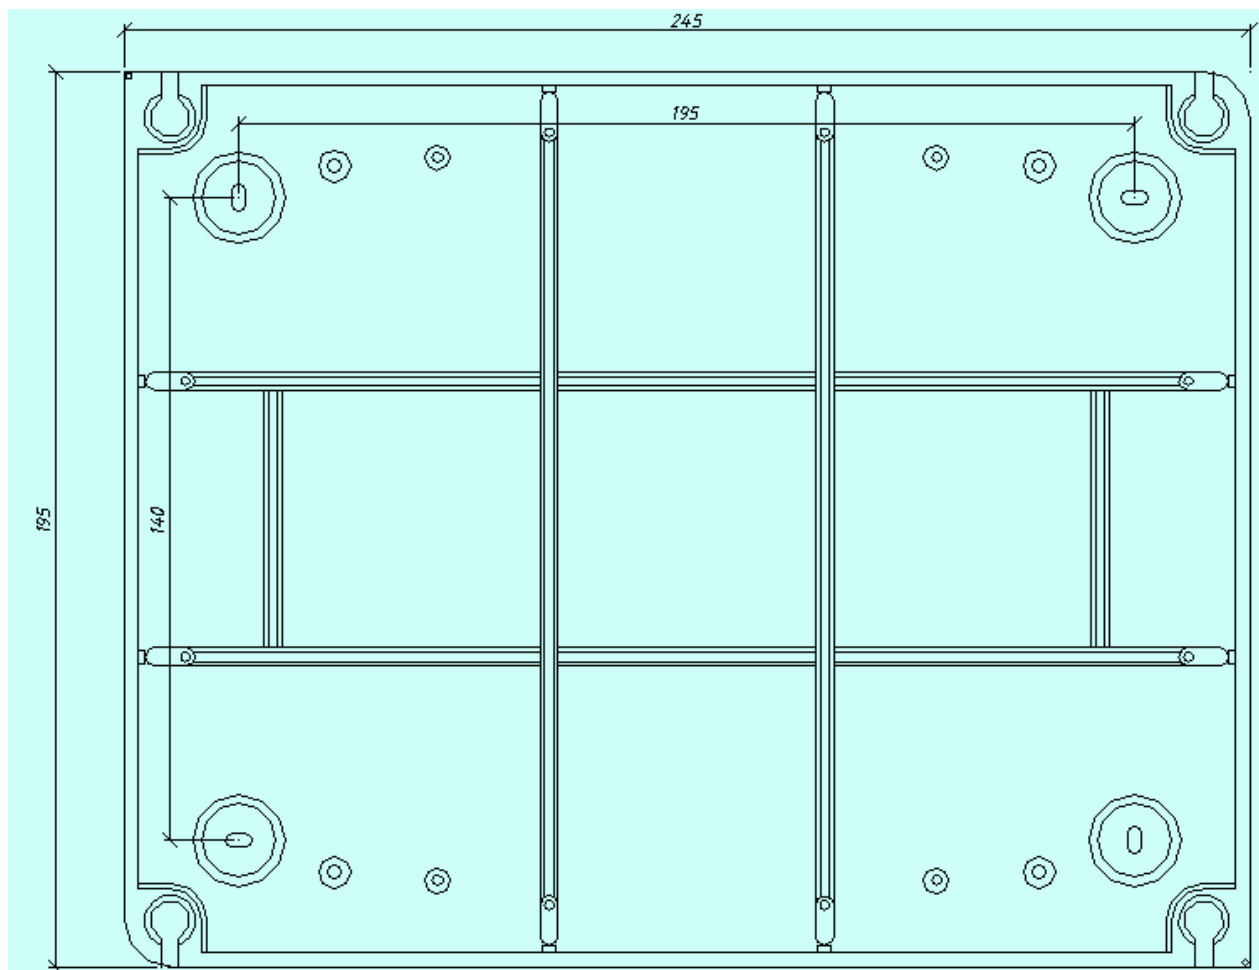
Габаритные и установочные размеры блока «БАКС-10»
